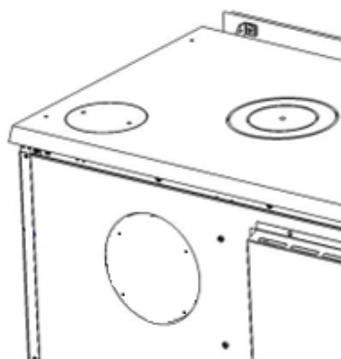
Entfernen Sie das verzinkte Blech
